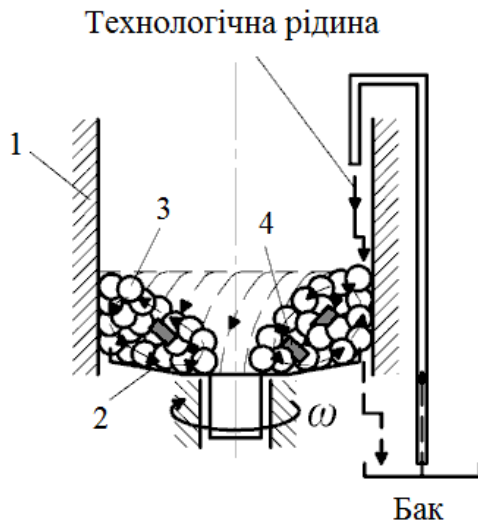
Схема відцентрово-ротаційної обробки
